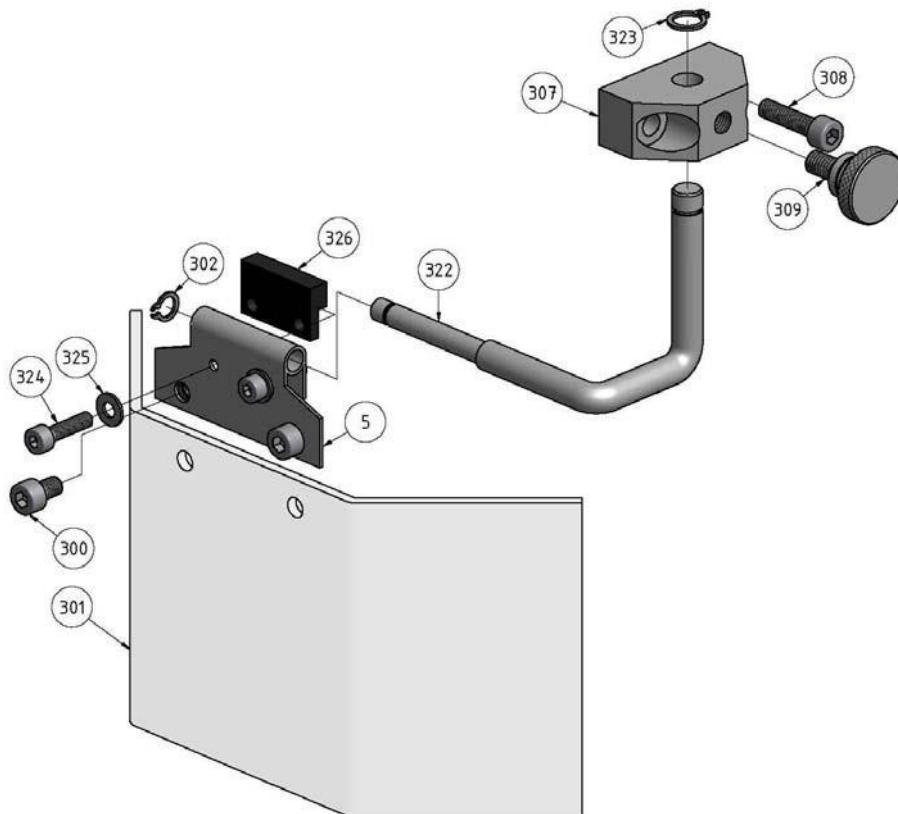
Fräsfutterschutz - Milling chuck protection
